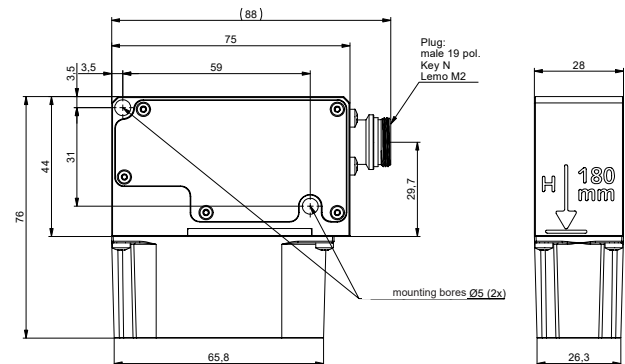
Abmessungen Correvit SF-Motion Sensorkopf
